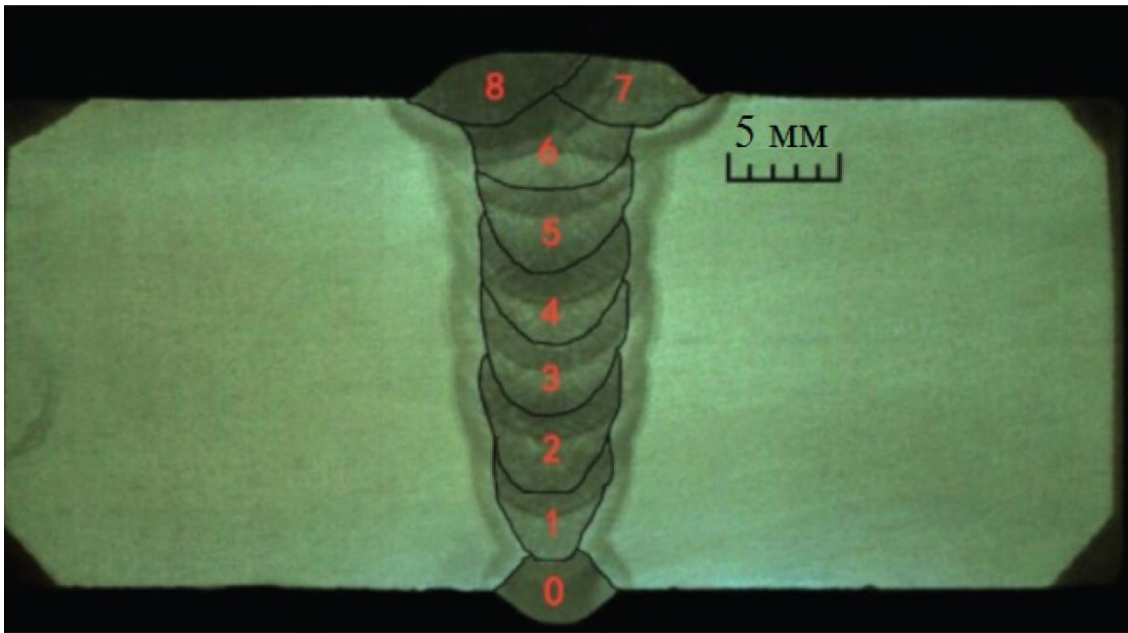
Поперечний мікрошліф кільцевого зварного з'єднання труб з вузькою обробкою крайок
